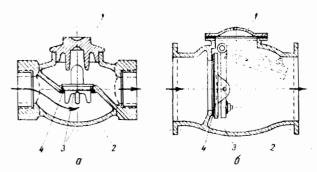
Обратные клапаны: а — подъемный, 6 — поворотный; 1 — крыпика корпуса; 2 — корпус; 3 — тарелка (захлопка); 4 — седло.
